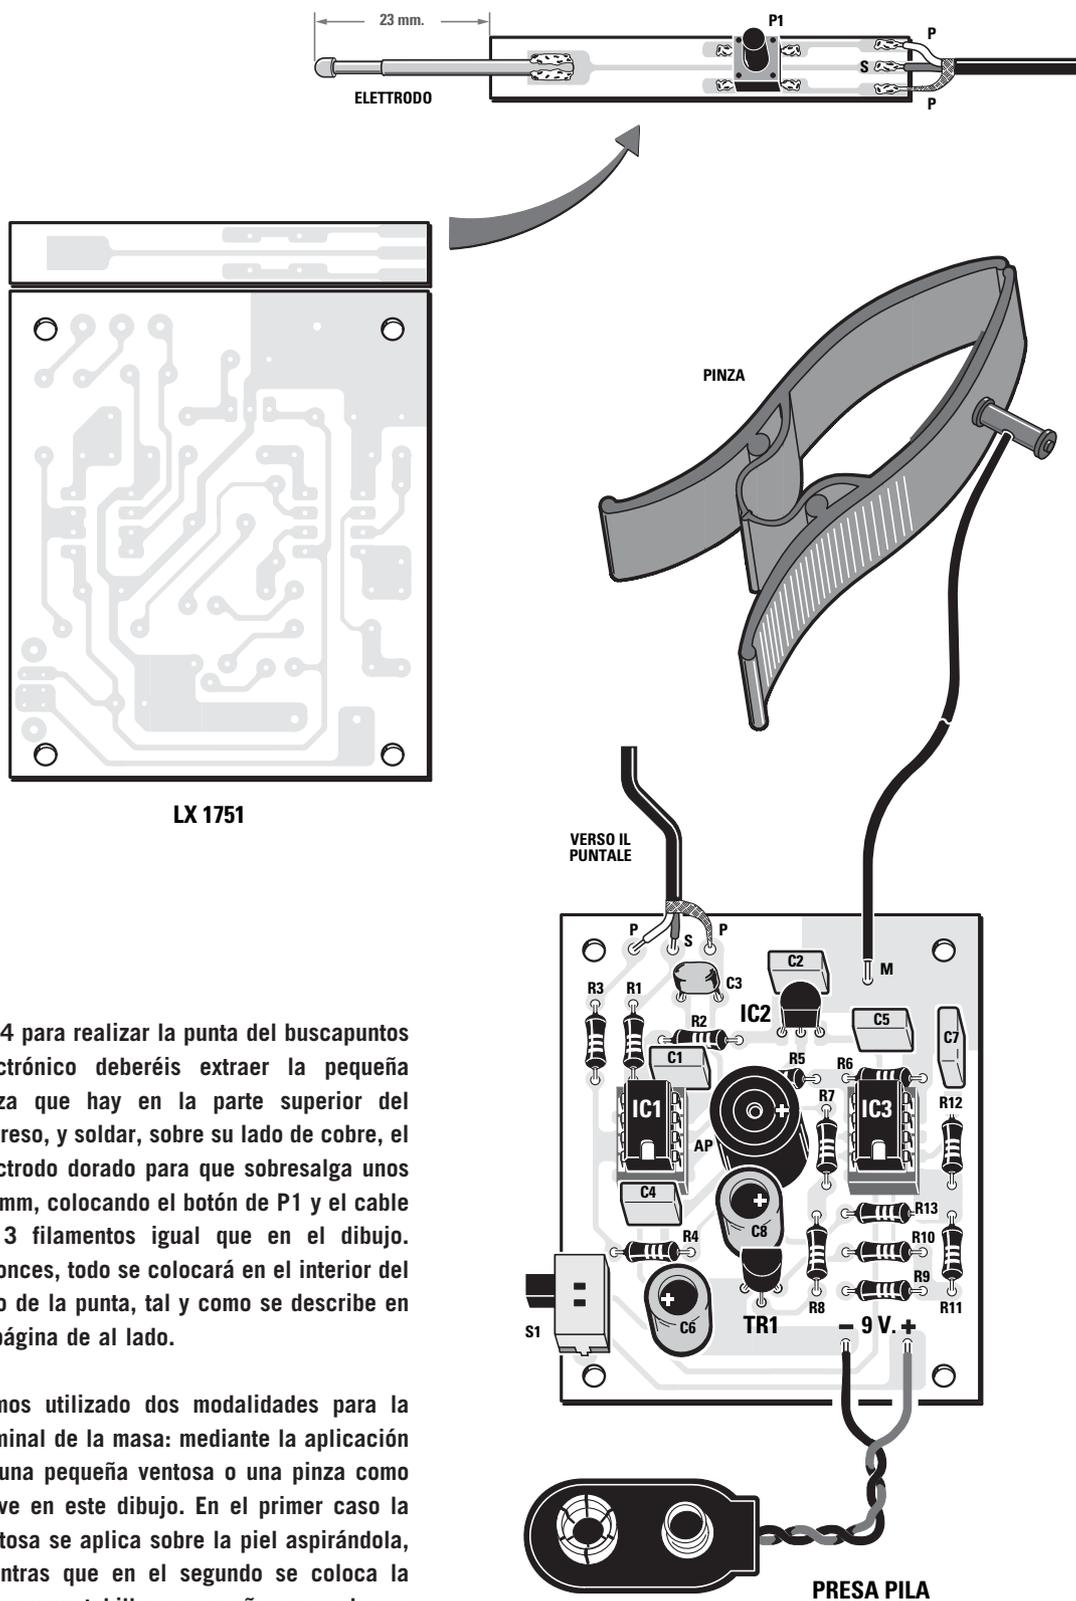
para realizar la punta del buscapuntos electrónico deberéis extraer la pequeña pieza que hay en la parte superior del impreso, y soldar, sobre su lado de cobre, el electrodo dorado para que sobresalga unos 23 mm, colocando el botón de P1 y el cable de 3 filamentos igual que en el dibujo. Entonces, todo se colocará en el interior del tubo de la punta, tal y como se describe en la página de al lado.
